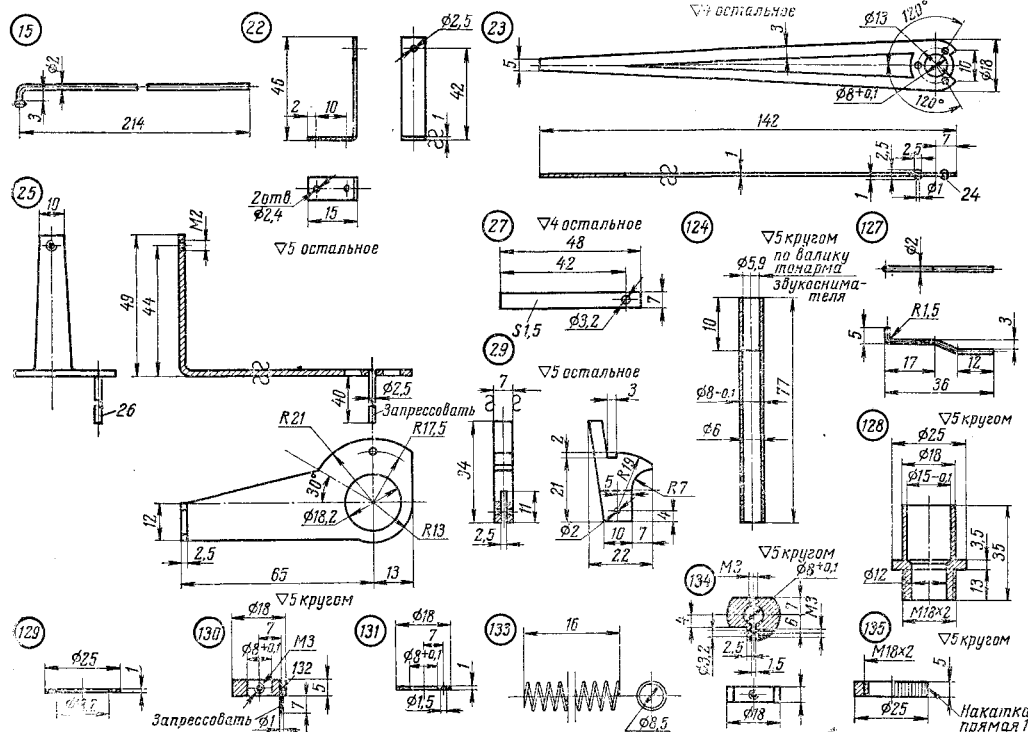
Детали механизма звукоусилителя: 15 — толкатель, спица велосипедная; 22 — кронштейн, Ст. 10 кп, закрепить на панели 61 заклепками 2,4×5; 23 — рычаг звукоусилителя, Д16А-Т; 24 — заклепки медные 1×3, 3 шт.; расклепать в детали 23; 25 — кронштейн, АМЦА-П; 26 — штифт, Ст. 45, запрессовать в деталь 25; 27 — пластина, Ст. 10 кп, крепить в детали 134 винтом М3×3; 29 — упор звукоусилителя, гетинакс, текстолит; 124 — полая ось, Ст. 45; 127 — упор, проволока стальная, паять к скобе звукоусилителя (см. «Радио», 1971, № 9); 128 — корпус, Ст. А12, никелировать; 129 — шайба, гетинакс, 2 шт.; 130 — кольцо, Ст. А12; 131 — шайба, гетинакс, 2 шт.; 132 — штифт, проволока стальная, запрессовать в деталь 130; 133 — пружина, проволока стальная класса I диаметром 0,8 мм; 134 — кольцо разрезное, Ст. А12; 135 — гайка, Ст. А12.
